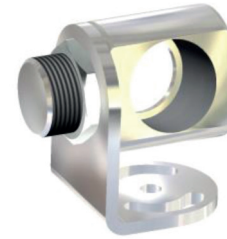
Montagebolzen mit M12x1-Gewinde,
